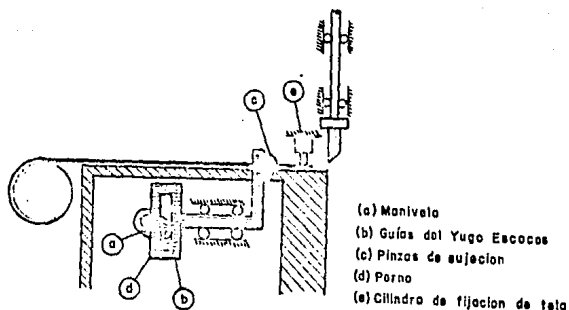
SISTEMA DE CORTE DE TELA CON ALIMENTADOR MECÁNICO
